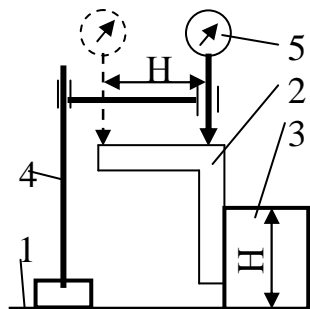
Схема для визначення відхилення від перпендикулярності: 1 – поверочная плита; 2 – поверочный угольник; 3 – деталь; 4 – штатив; 5 – измерительная головка
